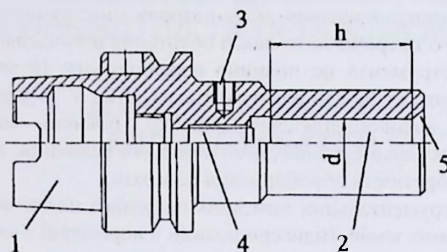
Конструкція затискного патрона із тепловою посадкою інструмента: 1 – конус HSK-A; 2 – отвір для посадки інструмента; 3 – отвори для балансувальних гвинтів; 4 – установочний гвинт; 5 – західна фаска.
